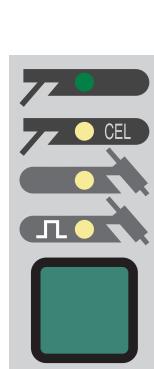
Soldadura por eléctrodo de barra: ajuste do parâmetro Dinâmica
